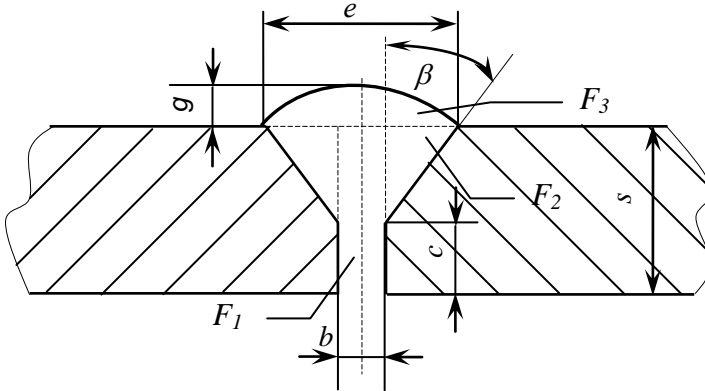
Эскиз сварного соединения (на примере стыкового соединения С17)
